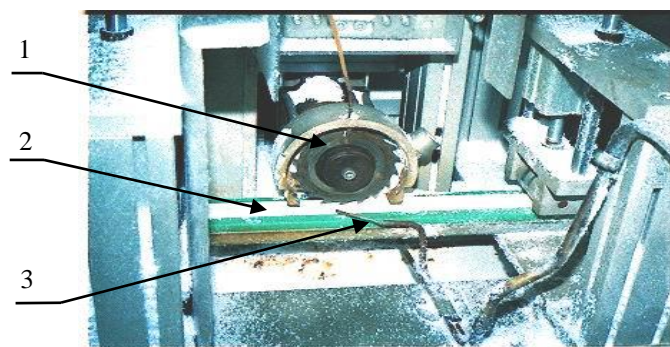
Установка «Agne Maschinen – und Stantlban» для непрерывного фрезерования канавки:
